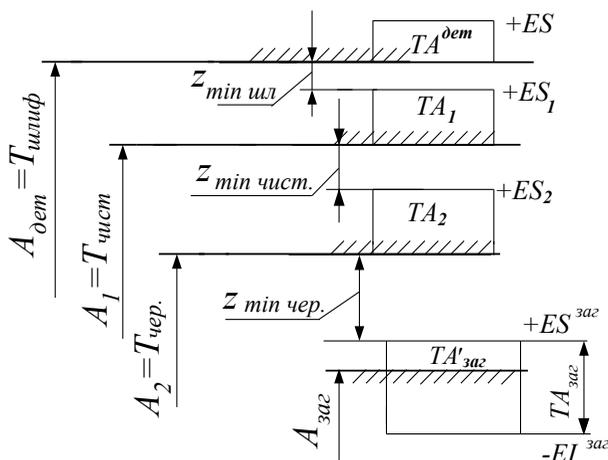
Расчетная схема для определения размера отверстия в заготовке с использованием минимальных припусков (охватывающий размер детали)
